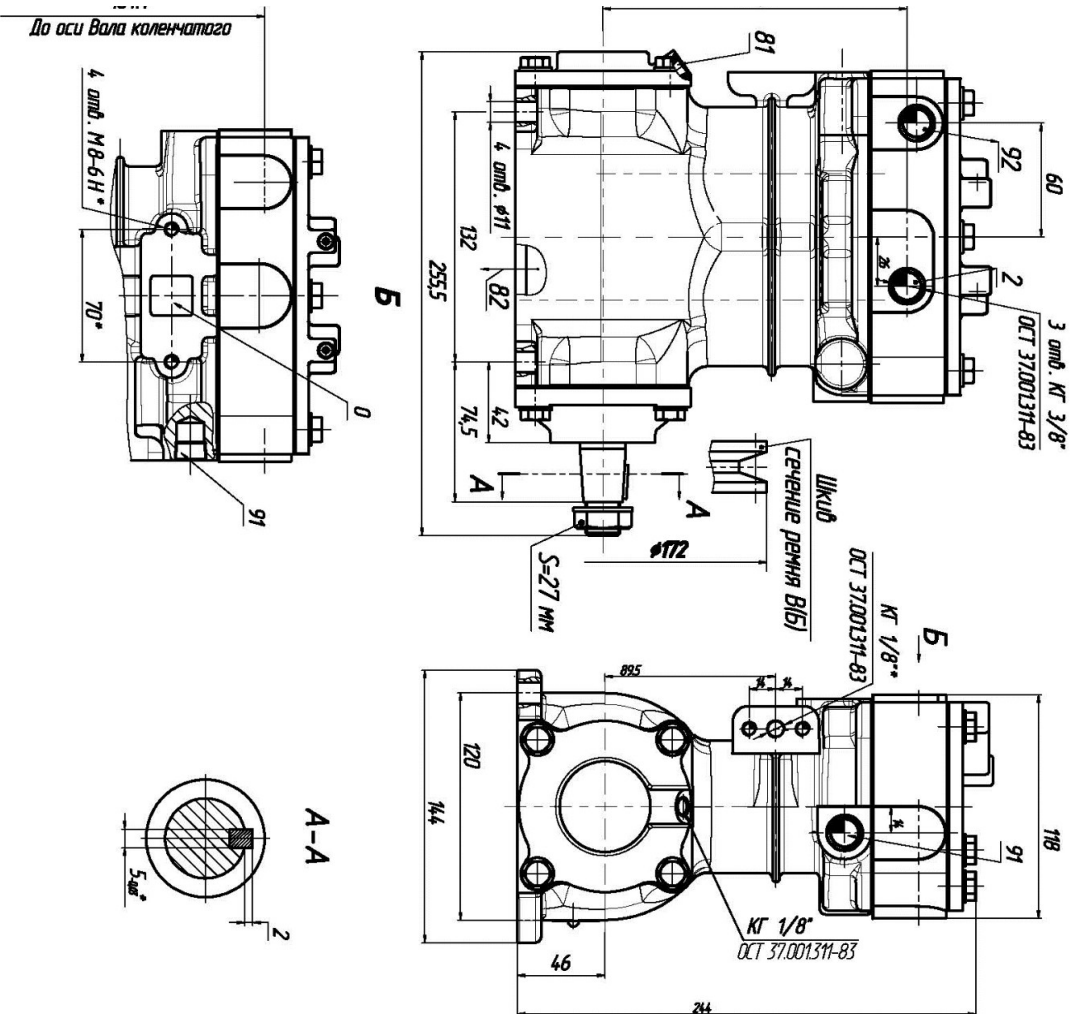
Присоединительные и установочные размеры компрессора
